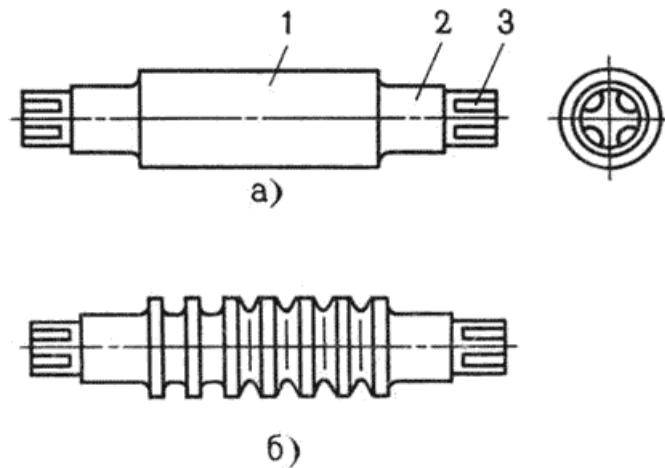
Прокатные валки: а – гладкий; б – калиброванный
